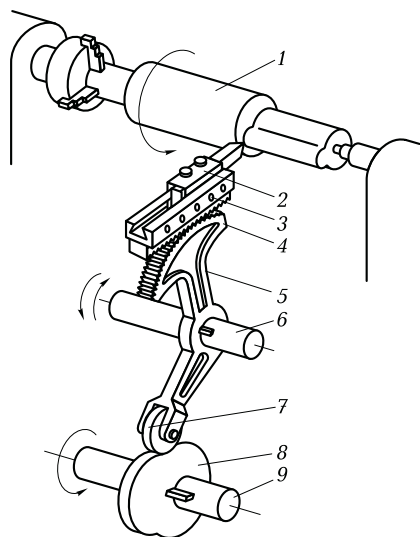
Приспособление с реечно-зубчатой и кулачковой передачами:
